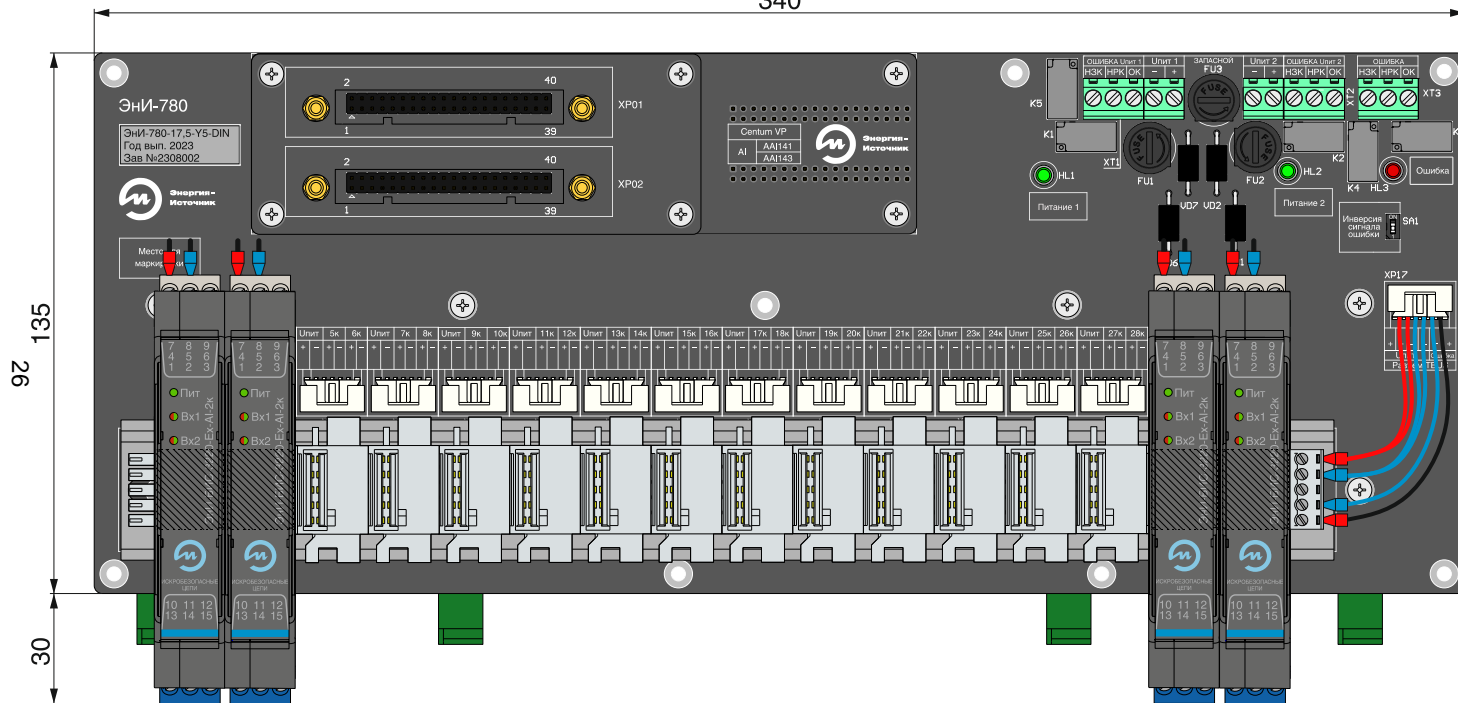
Габаритные размеры платы для шестнадцати приборов с корпусом шириной 17,5 мм
